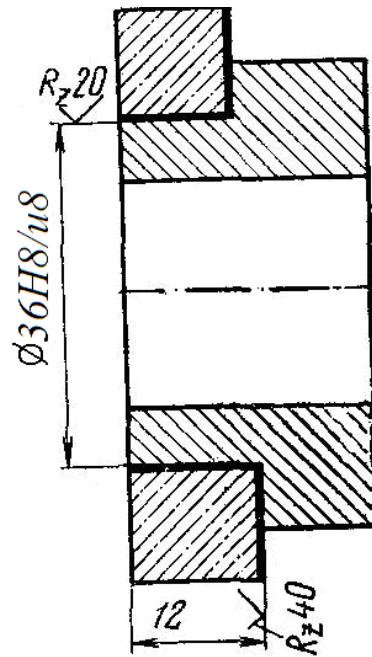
Ескіз підготовки деталі до ремонту із заштрихованою частиною, що видаляється
